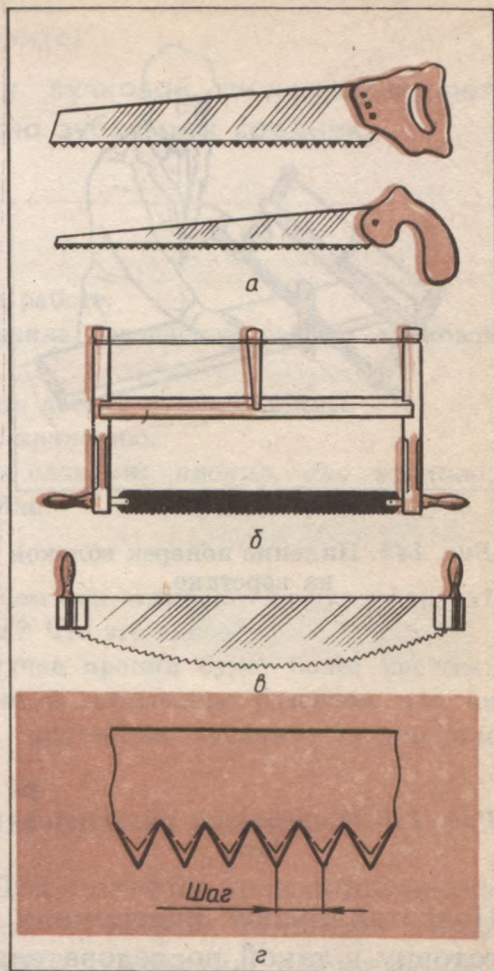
Пилы для пиления древесины поперек волокон: а — ножовка; б — лучковая; в — двуручная; г — форма зубьев поперечной пилы.
